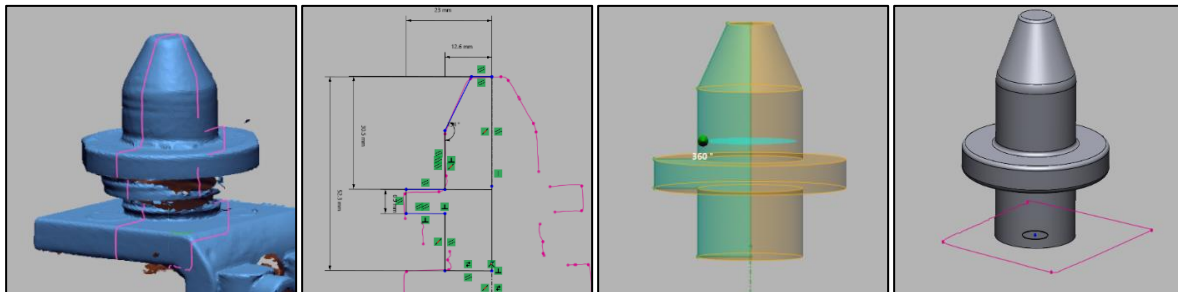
Diseño de una pieza del elemento 3. Fuente: Desarrollo propio
